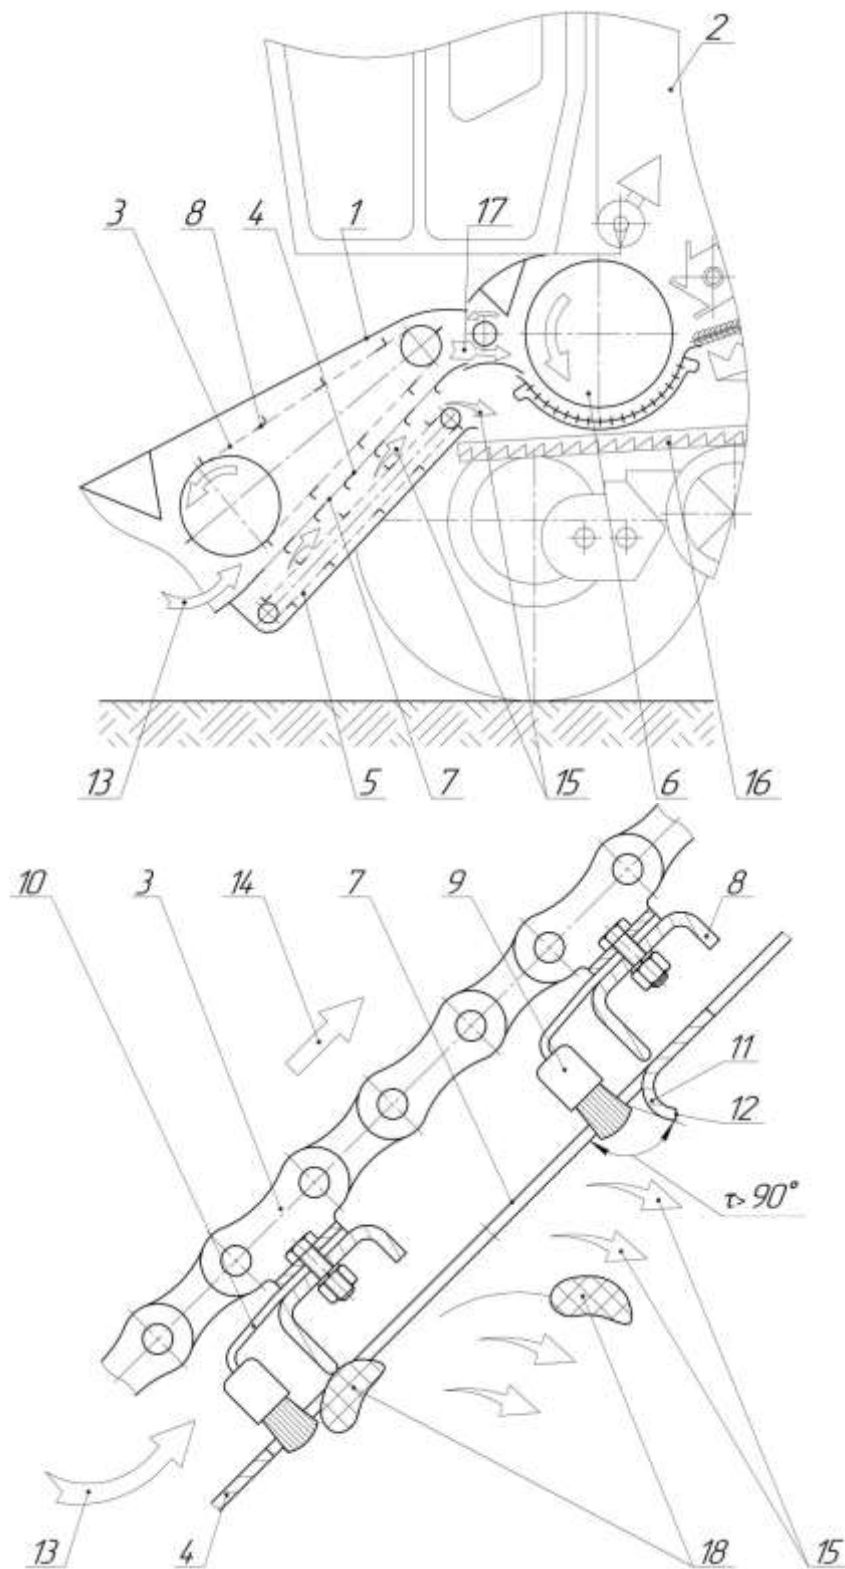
Наклонная камера зерноуборочного комбайна, оснащенная перфорированным днищем и приспособлением для его очистки (Патент РФ № 2725729): 1 – наклонная камера; 2 – комбайн; 3 – плавающий транспортер; 4 – решетчатое днище; 5 – устройство для отвода свободного зерна; 6 – молотильная камера; 7 – устройство для очистки отверстий; 8 – скребок; 9 – щетка; 10 – поводок; 11 – язычок; 12 – нижняя кромка; 13 – очесанный ворох; 14 – направление движения; 15 – мелкие примеси; 16 – транспортная доска; 17 – недомолоченные колоски; 18 – крупные включения
